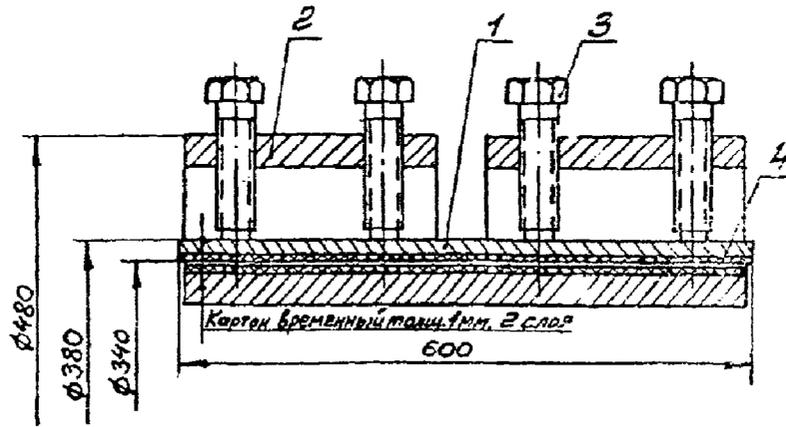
Приспособление для прессовки изоляции контактных колец:
